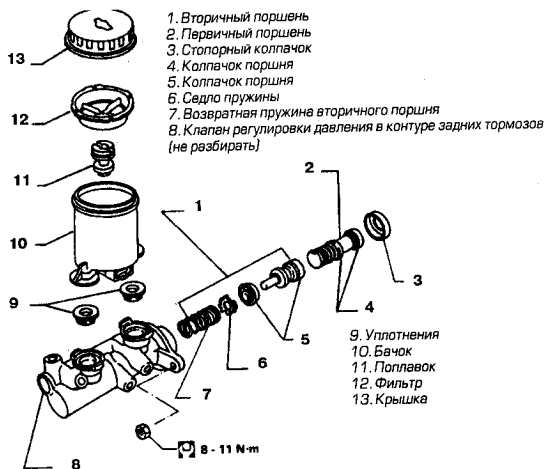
Элементы главного тормозного цилиндра (См. Раздел 9)
